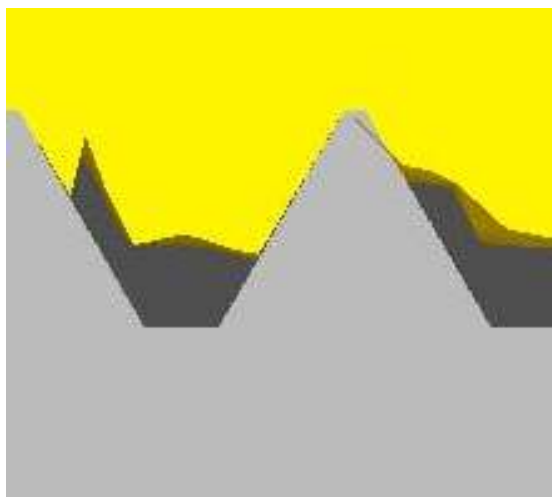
Фрагмент резьбы с зарождающейся складкой
